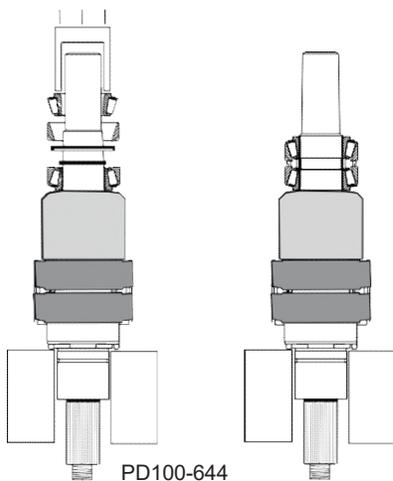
Ensemble roulement à rouleaux coniques arrière
